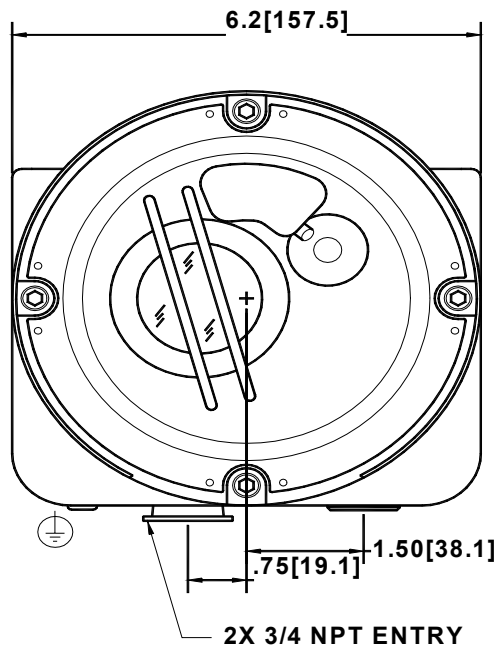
Габаритный чертеж FlameGard 5 UV/IR
